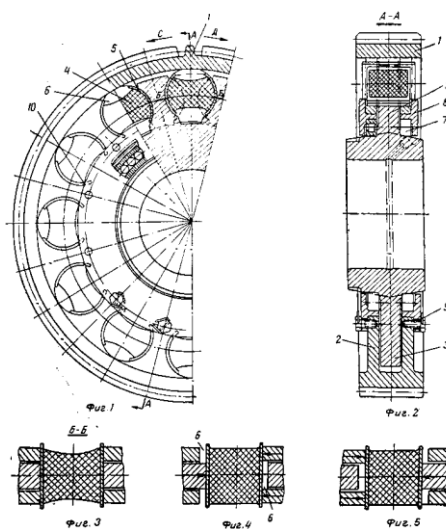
Пружне зубчасте колесо для тягової передачі локомотива
